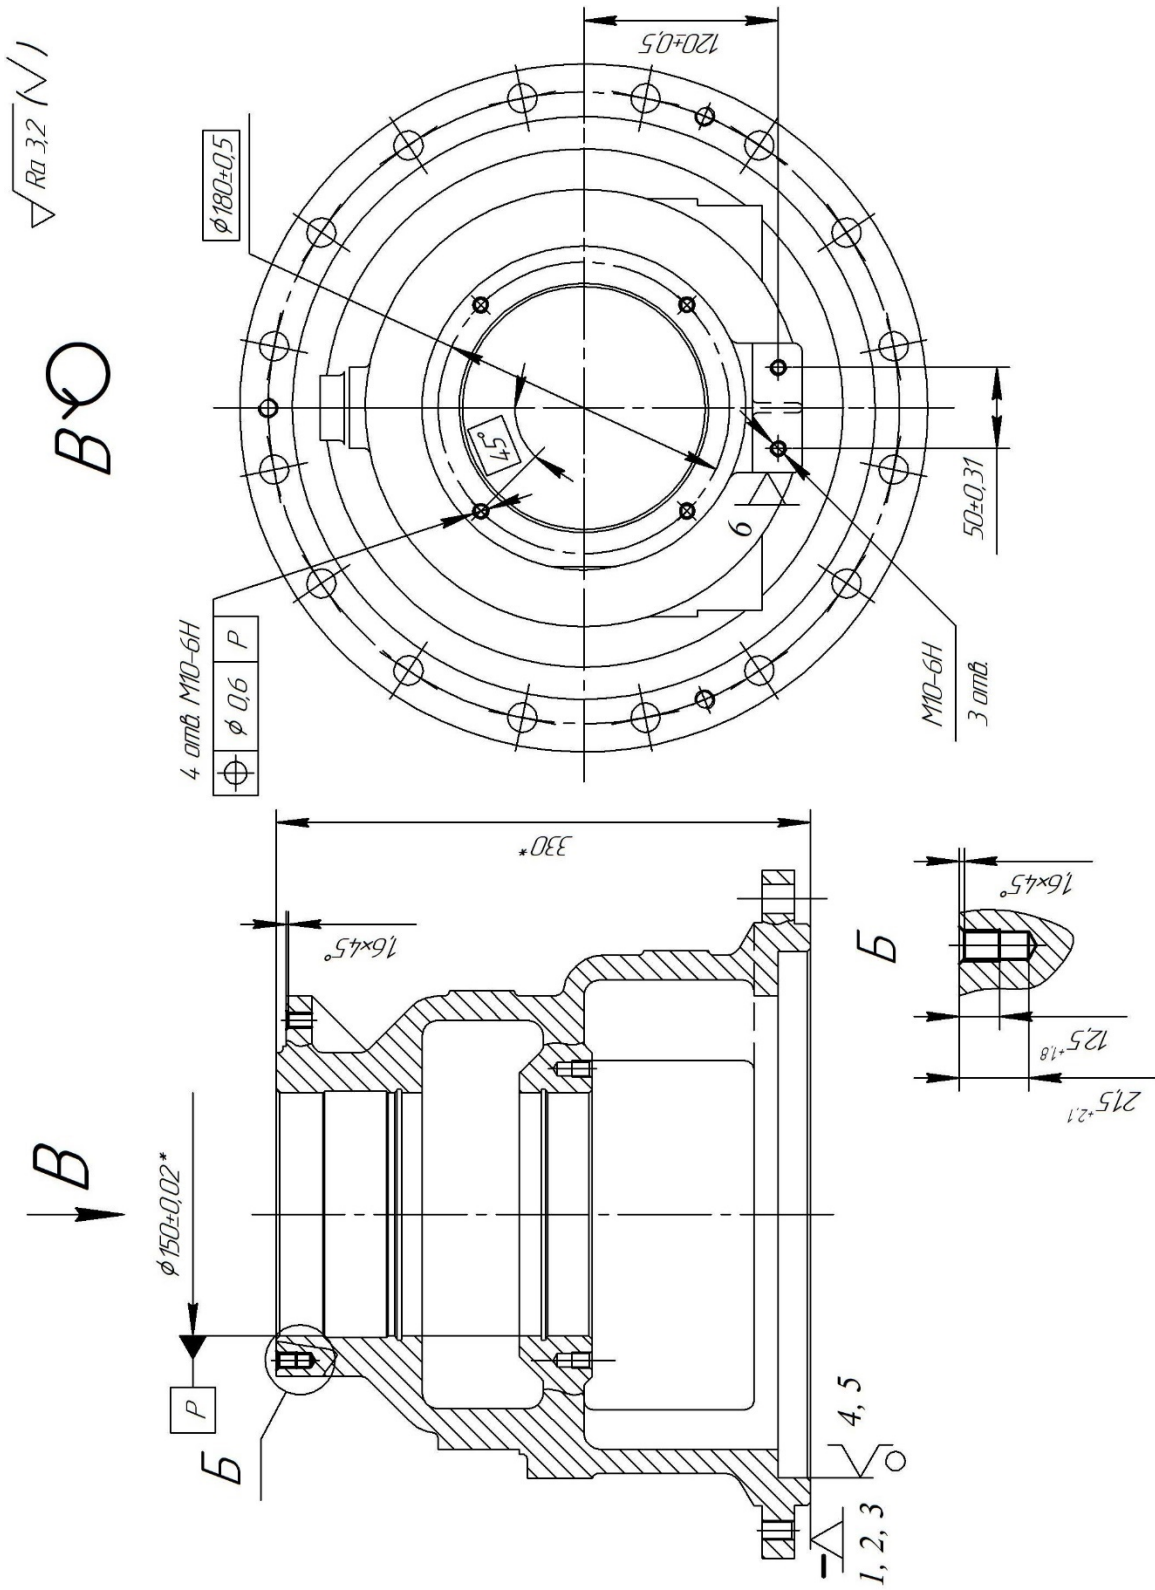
Схема базування заготовки на операції комплексній з ЧПК 045, установ Б
